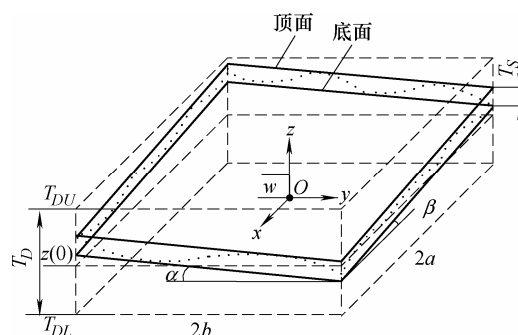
平面尺寸公差与形状公差的耦合公差域
